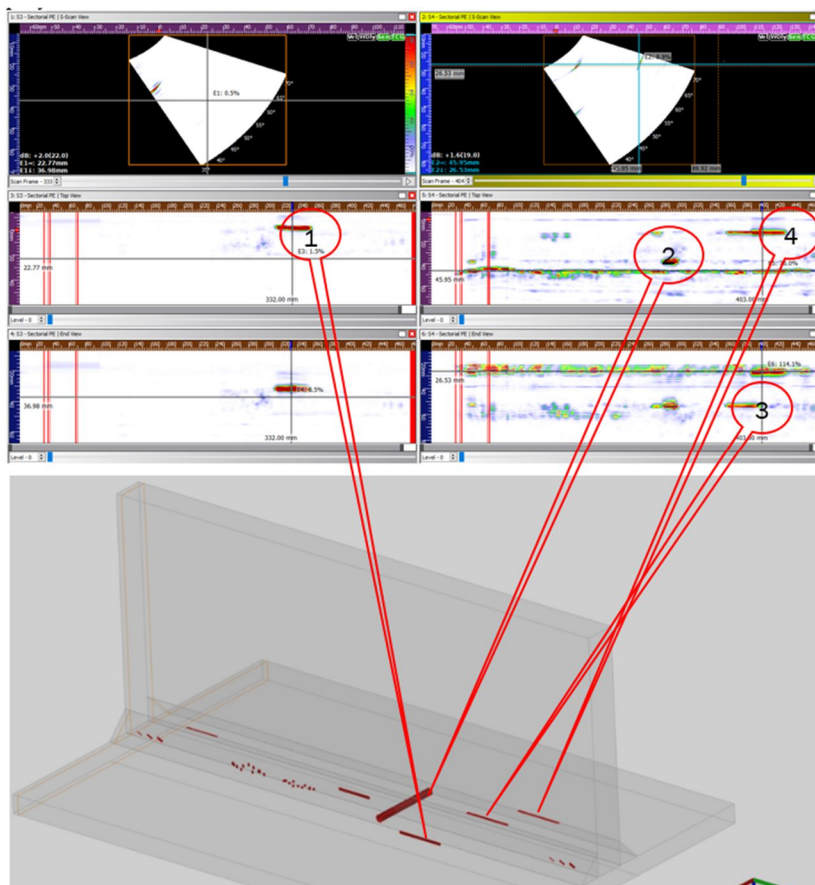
Сопоставление результатов контроля сварного соединения с конструктивным непроваром с эскизом образца
